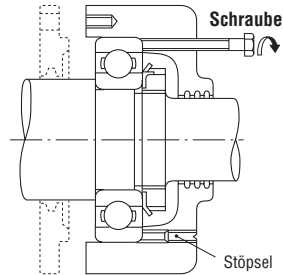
Demontage des Außenrings mittels Schrauben
